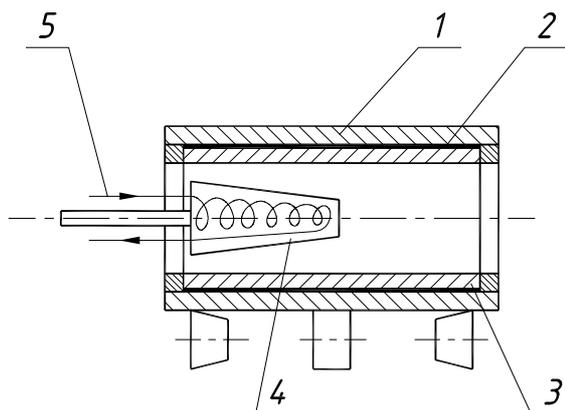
Центробежная отливка гильз цилиндров ДВС с принудительным охлаждением внутренней поверхности
